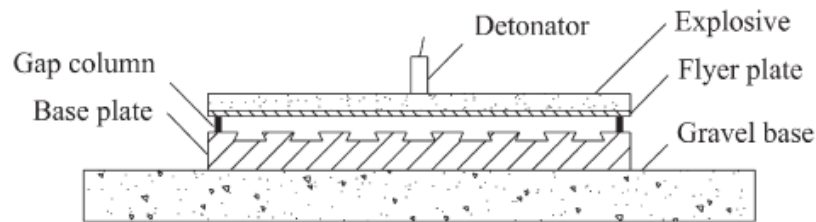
Soldadura por explosão utilizando entalhes na placa base (Li, et al., 2015).
